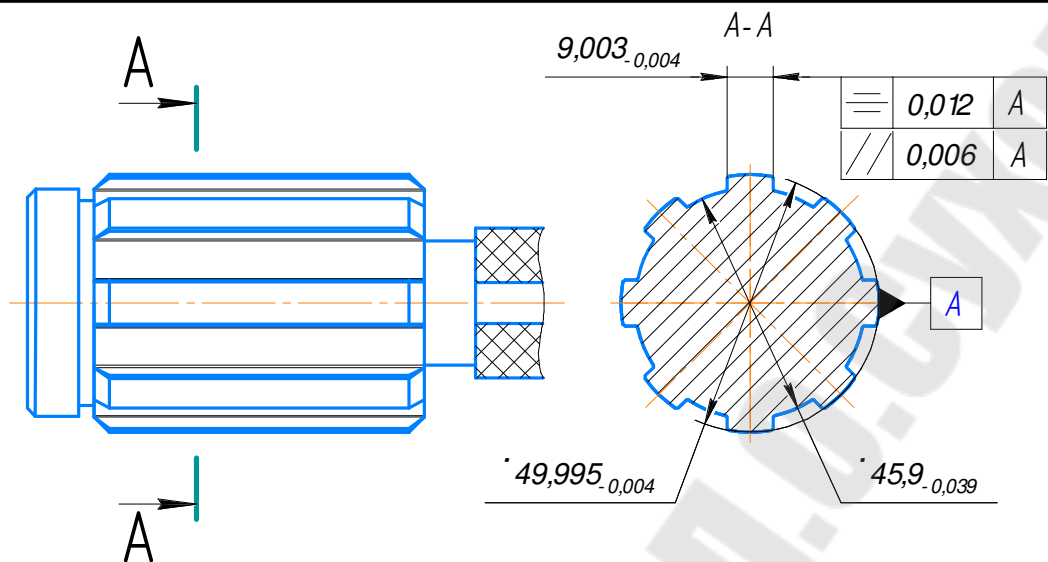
Эскиз калибра для контроля шлицевой втулки.
